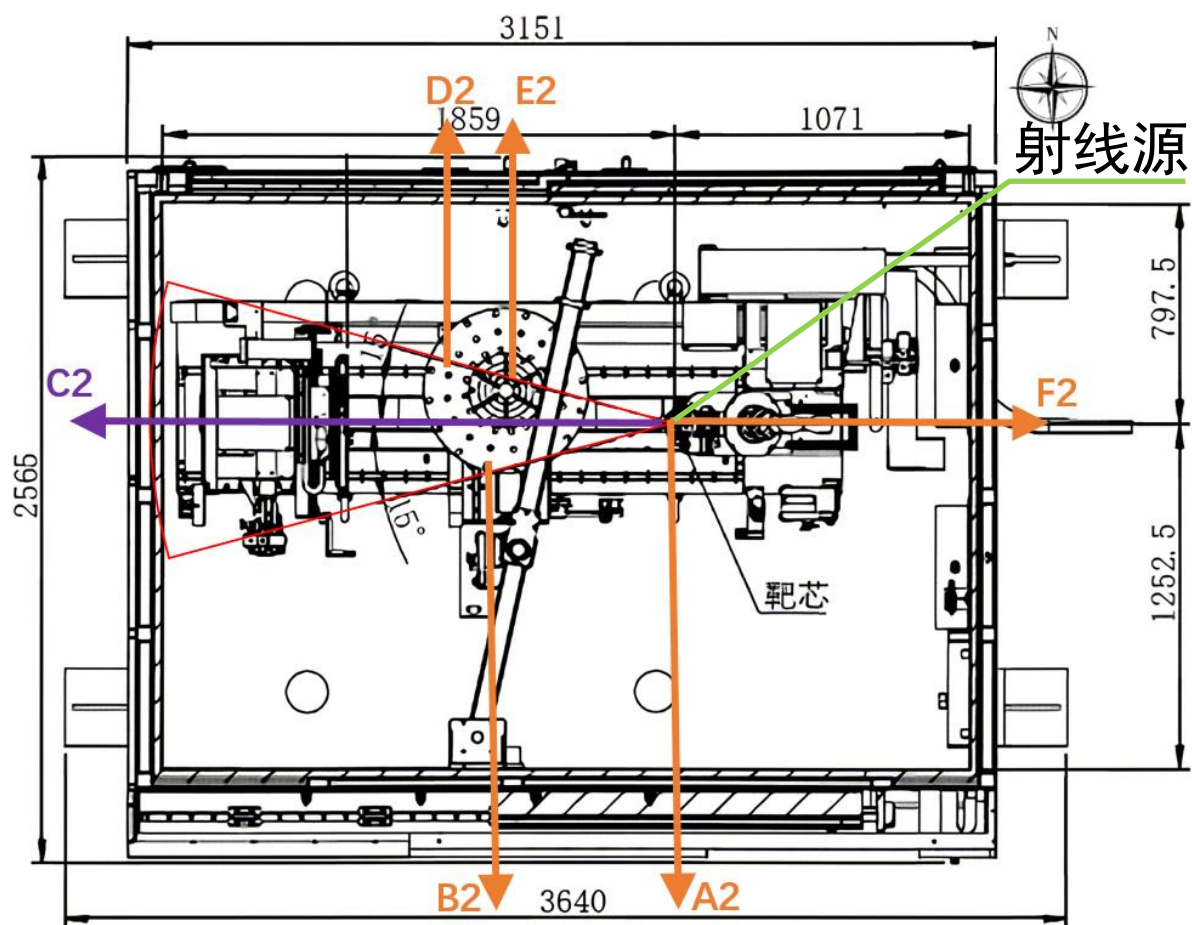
FXO-CT3000 型工业 CT 辐射屏蔽计算预测点位平面图 (单位: mm)
